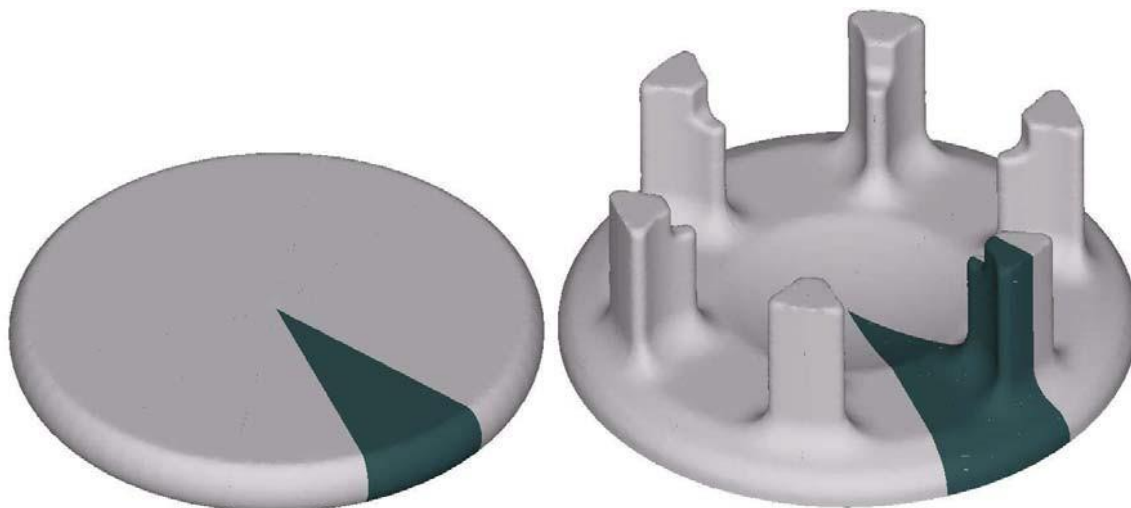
1\12 частина заготовки та штамповки
